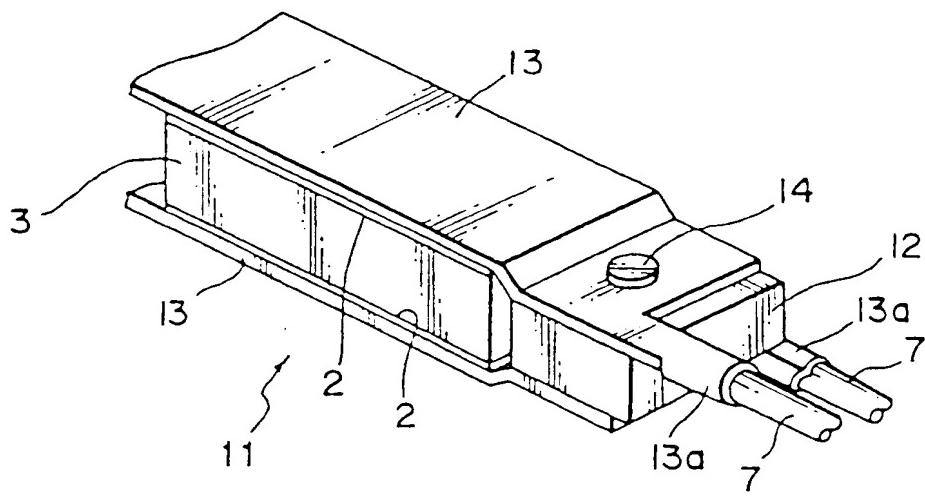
Stand der Technik*Fig. 2* Stand der Technik
